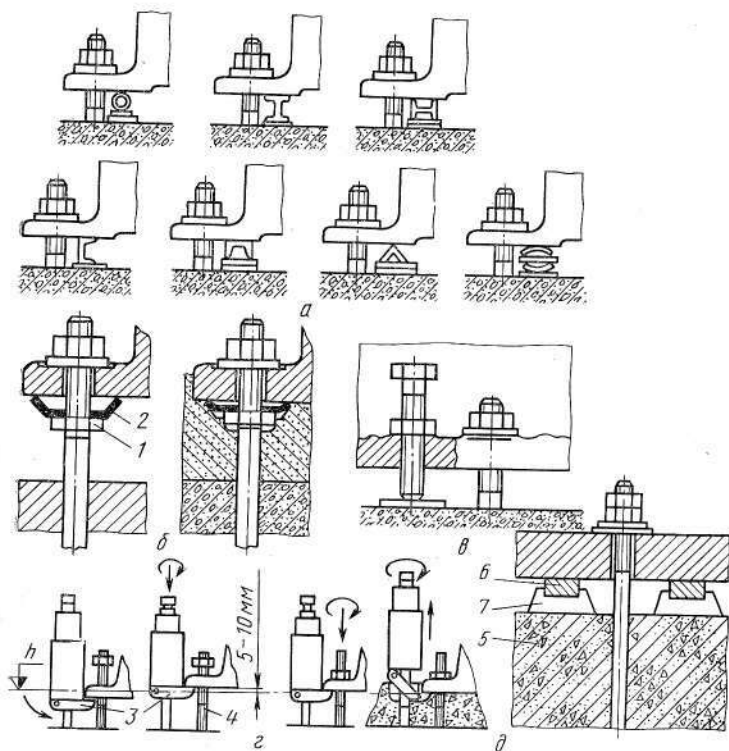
Схемы выверки оборудования при бесподкладочном монтаже: 1 — установочная гайка; 2 — тарельчатая шайба; 3 — домкрат с консольной опорой; 4 — фундаментный болт; 5 — фундамент; 6 — металлическая пластина; 7 — бетонная подушка
